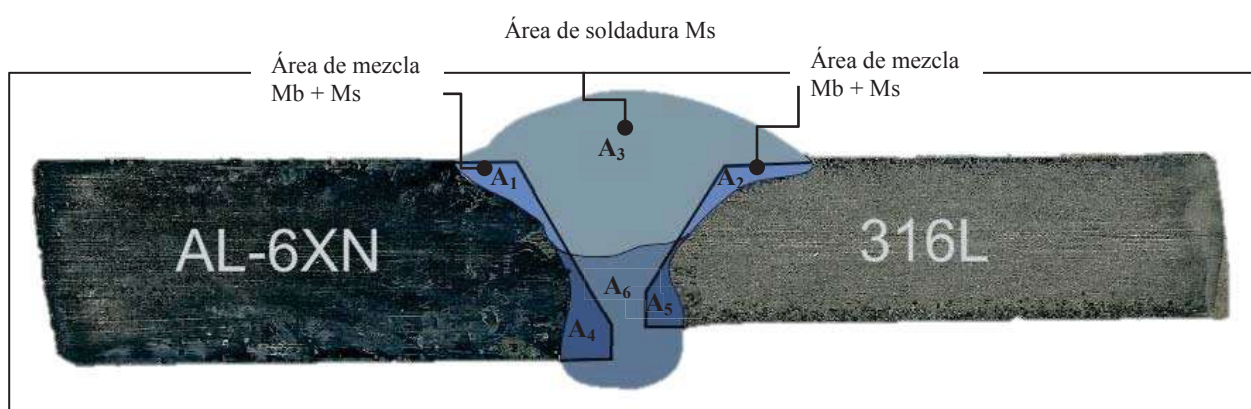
Dilución del metal de soldadura en la unión disímil de soldadura.
